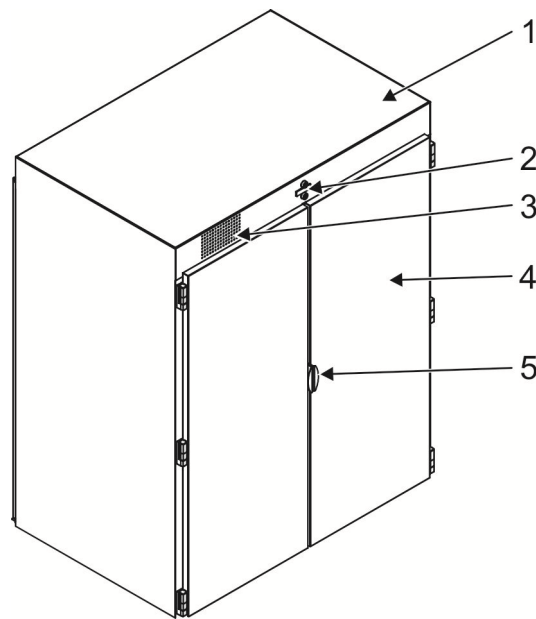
Vista d'insieme dell'armadio con passavivande 9 StE
